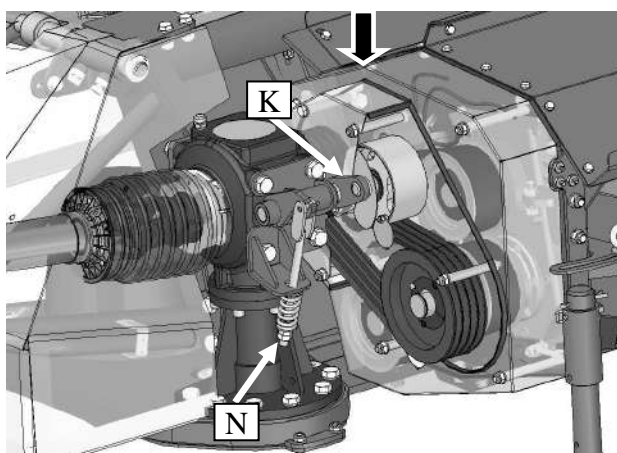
Регулировка напряжения ремня ременной передачи (вид без части защит) – валики покоса
